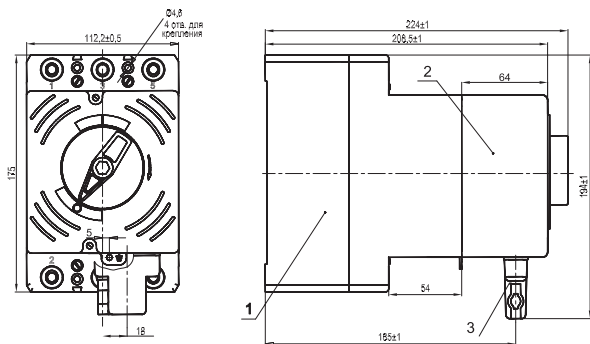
Расположение отверстий для крепления выключателя
